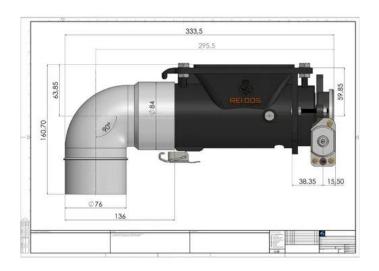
Desenho técnico do Alimentador Automático Para peixes
